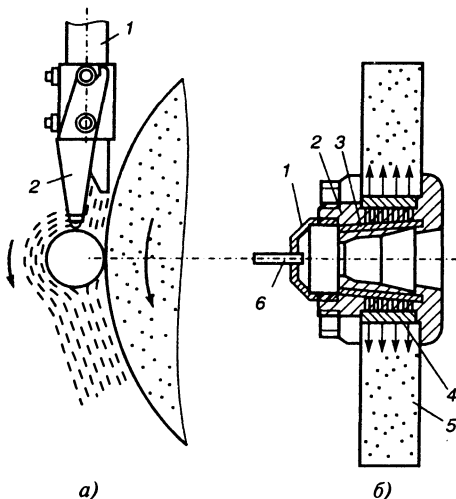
Конструкции устройств для подачи СОЖ при шлифовании:
